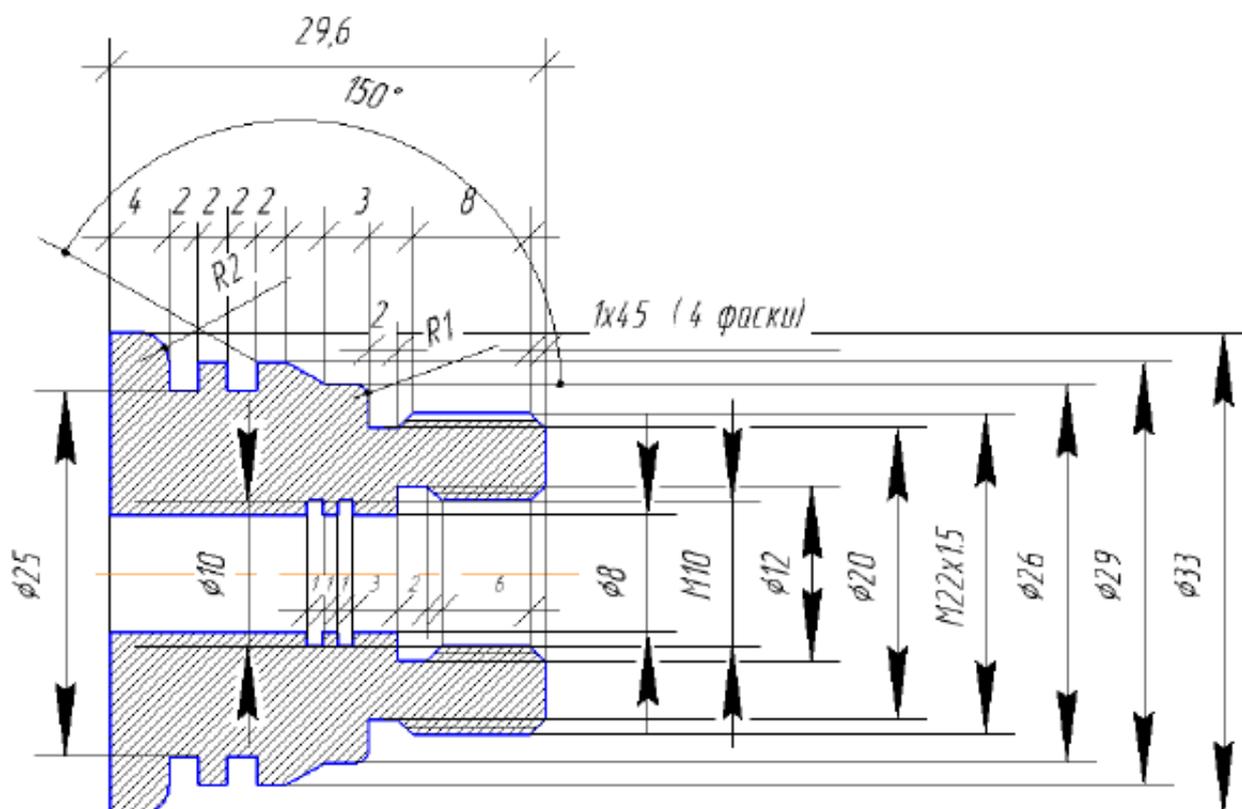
Чертеж детали (материал: Сталь 30ХГСА).
